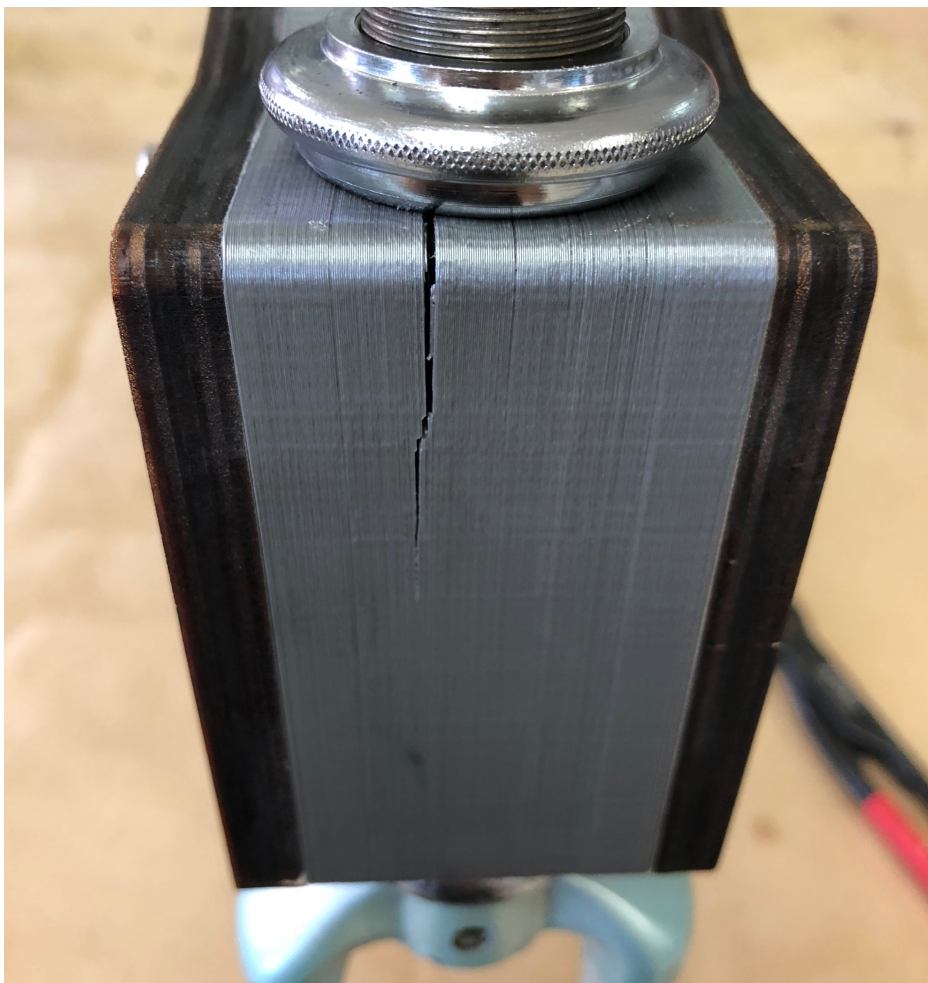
Fractura en la pieza delantera impresa en 3D. Fuente: (elaboración propia)
